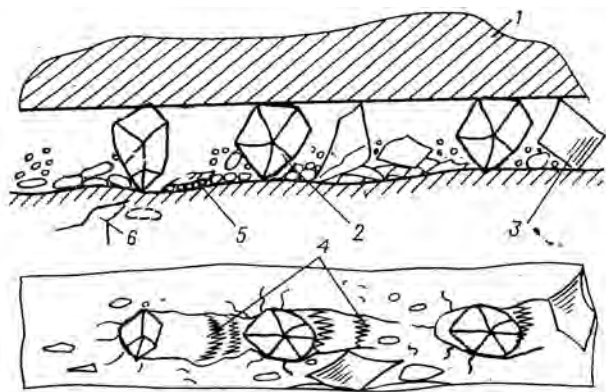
Схема разрушения заготовки при распиливании: 1 – режущий инструмент; 2 – алмазные зерна; 3 – расколовшиеся алмазные зерна; 4 – чешуйки спрессованного материала образца; 5 – слой раздавленного материала образца; 6 – трещины
